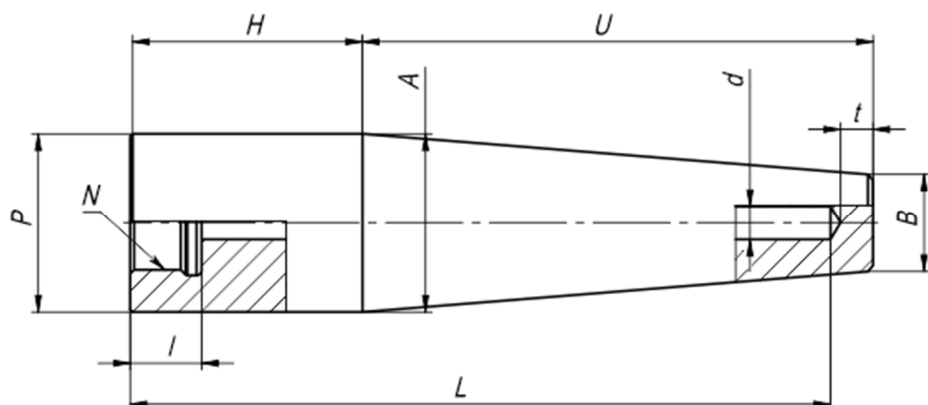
Гильза под приварку в стенку трубопровода (Weld-in), цельноточёная, коническая, под неподвижный штуцер.
